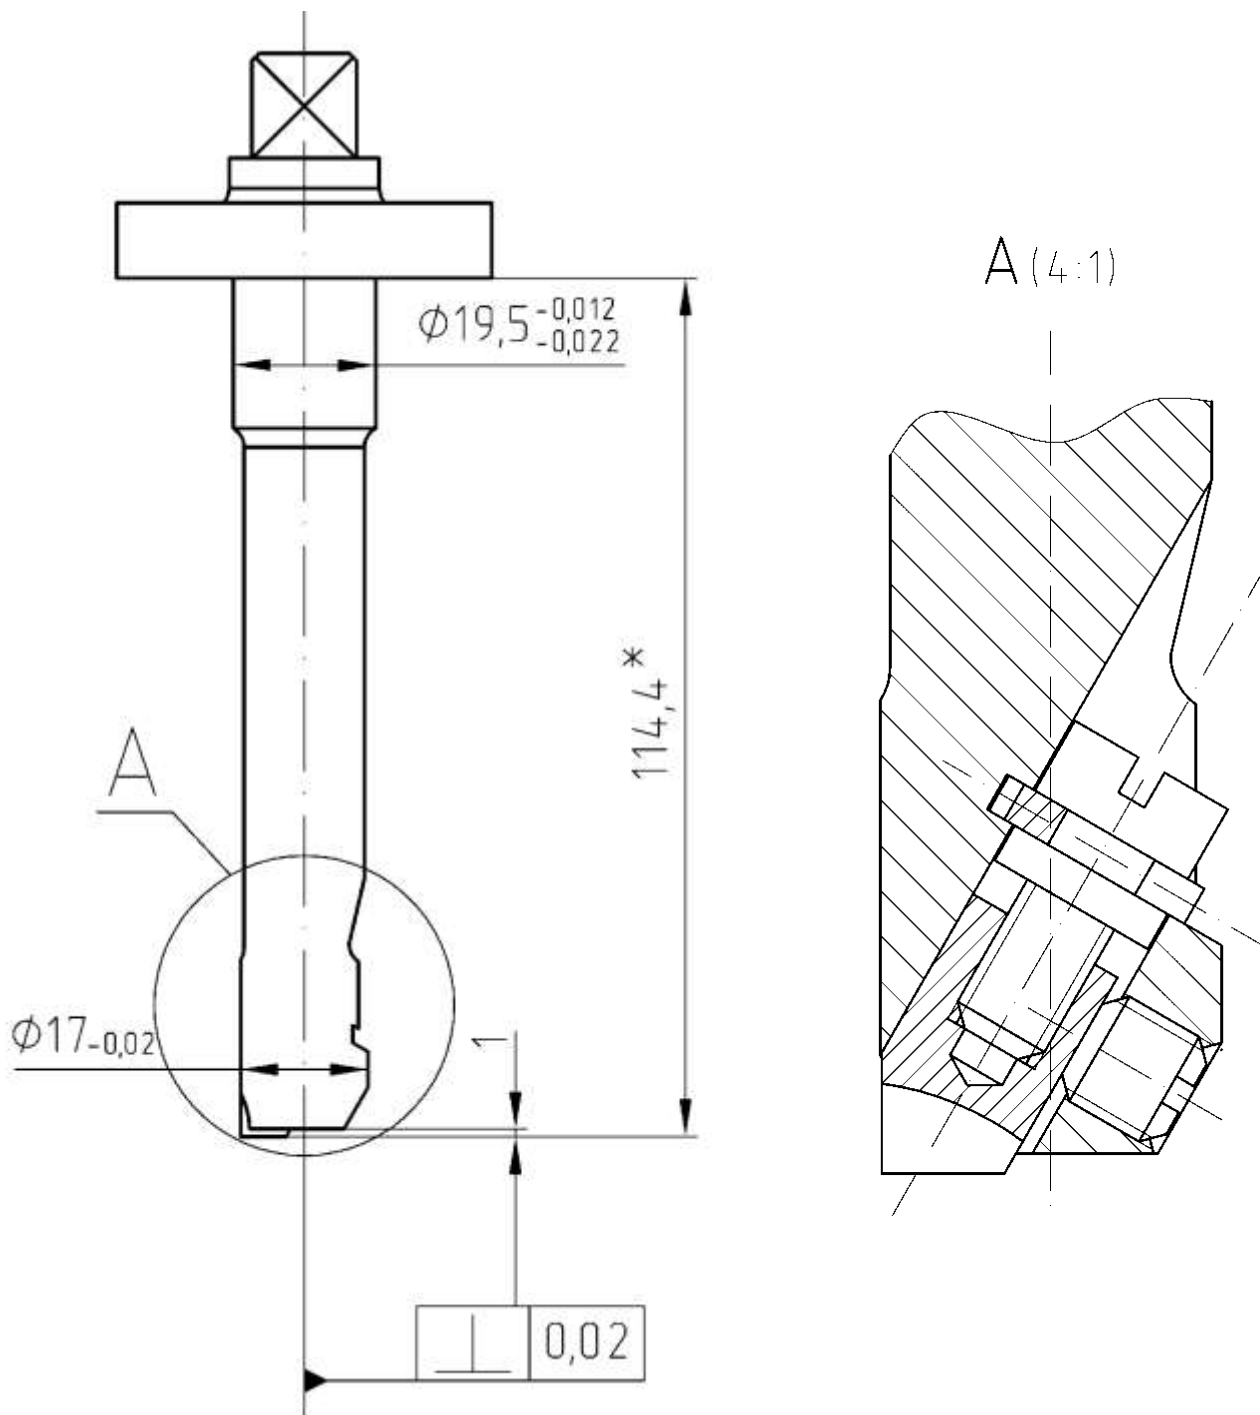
27-Ф-3871 Резец для подрезки торца под уплотнительное кольцо топливной форсунки
